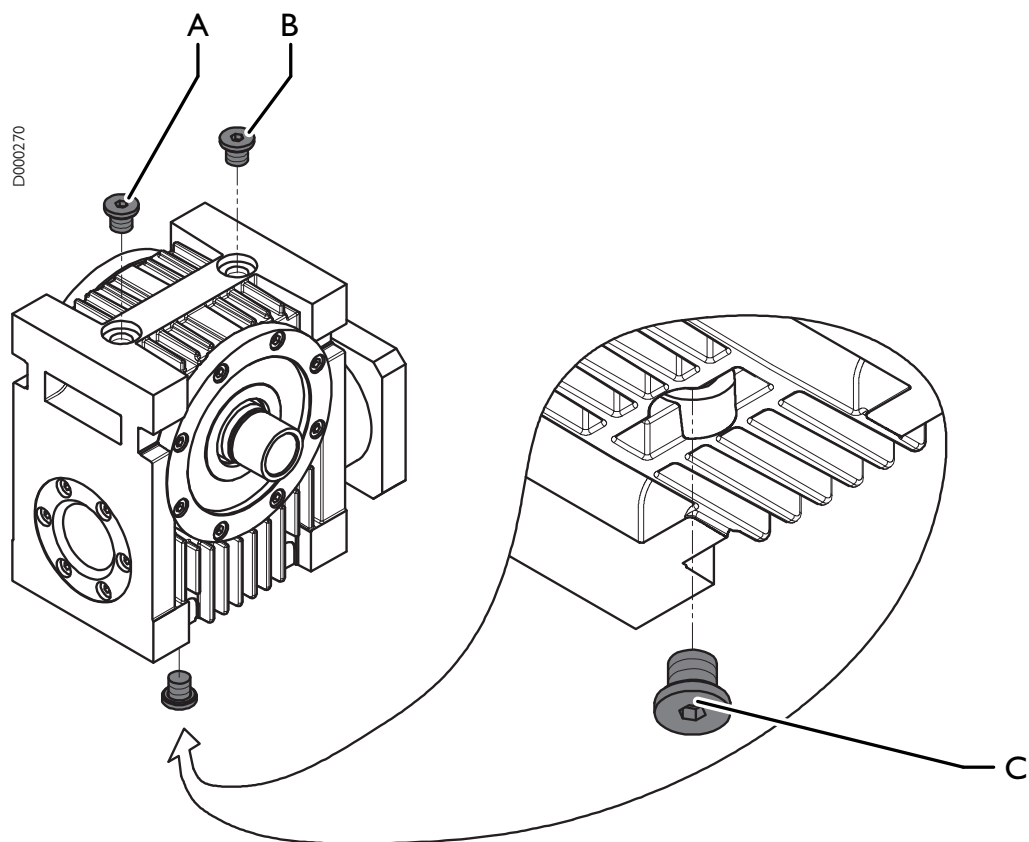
Смазочный материал заменить: Блок редуктора Güdel
